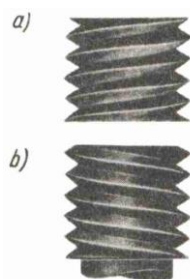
Przykład gwintu naciętego na powierzchni walcowej
